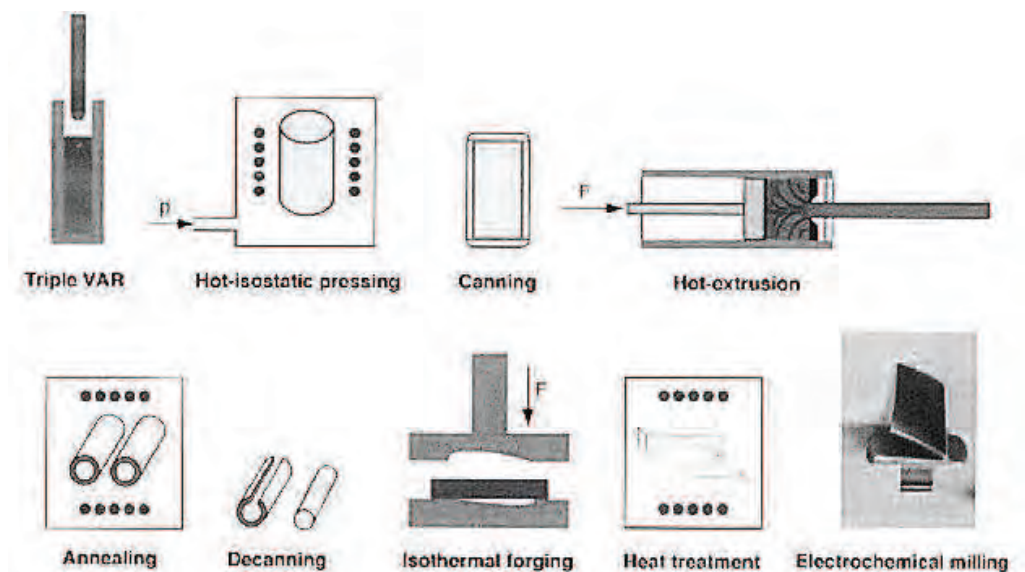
Processus de fabrication par forgeage d'aubes de turbine de compresseurs [94, 138].
